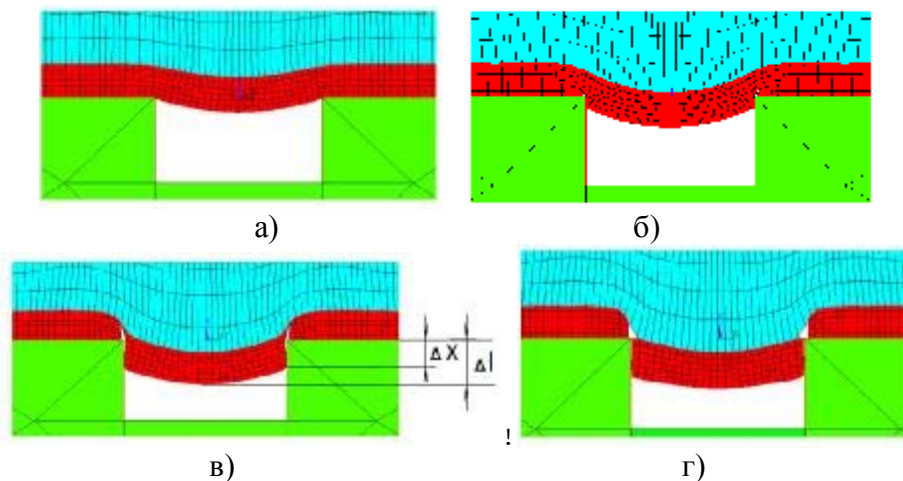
Поэтапное разделение фрагмента заготовки при вырубке детали на локализованном инструменте без дополнительной опоры
